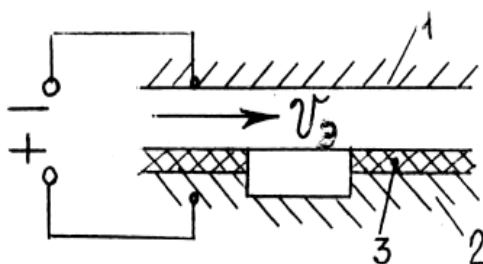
Схема обробки з нерухомими електродами: 1 – електрод-інструмент; 2 – заготовка; 3 – діелектрик
